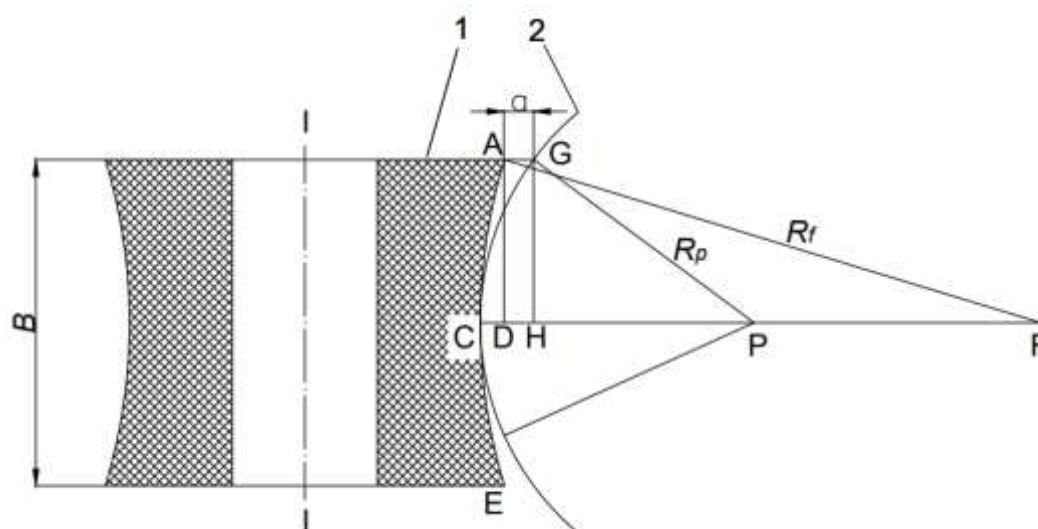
Схема для расчетов зазора a при зачистке поверхности детали с радиусом поперечной кривизны меньше радиуса кривизны профиля лепесткового круга, где 1 – профилированный лепестковый круг; 2 – обрабатываемая поверхность; А – максимальный зазор; В – ширина лепесткового круга; R_f – радиус профиля лепесткового круга; R_p – радиус кривизны детали
